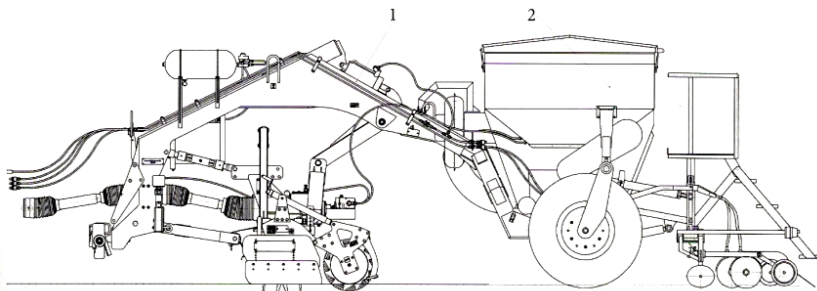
Общий вид агрегата почвообрабатывающе-посевного АППА-4 с активными рабочими органами: 1 – адаптер почвообрабатывающий; 2 – сеялка
